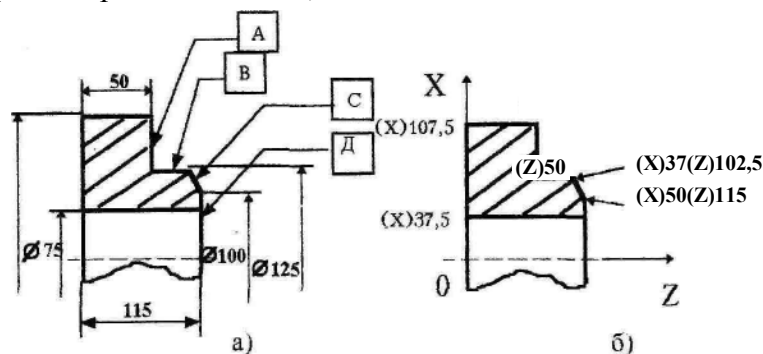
Чертеж заготовки (а) и ее размеры в абсолютных координатах (б)
